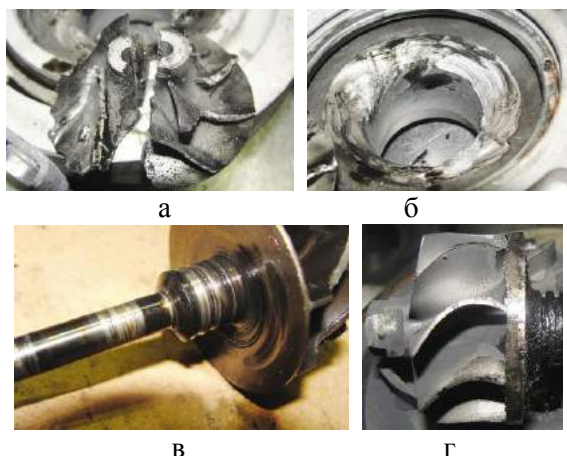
Разрушенное колесо компрессора: а – поврежденный корпус; б – перегрев и повреждение подшипников, вала; в – перегрев и повреждение лопаток турбины; г –
